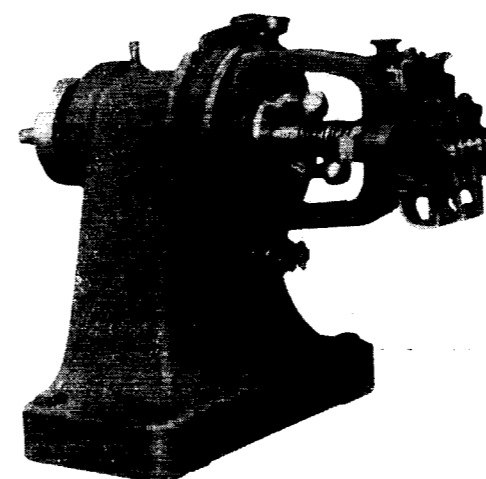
Interruptor centrífugo sin la tapa de protección.
